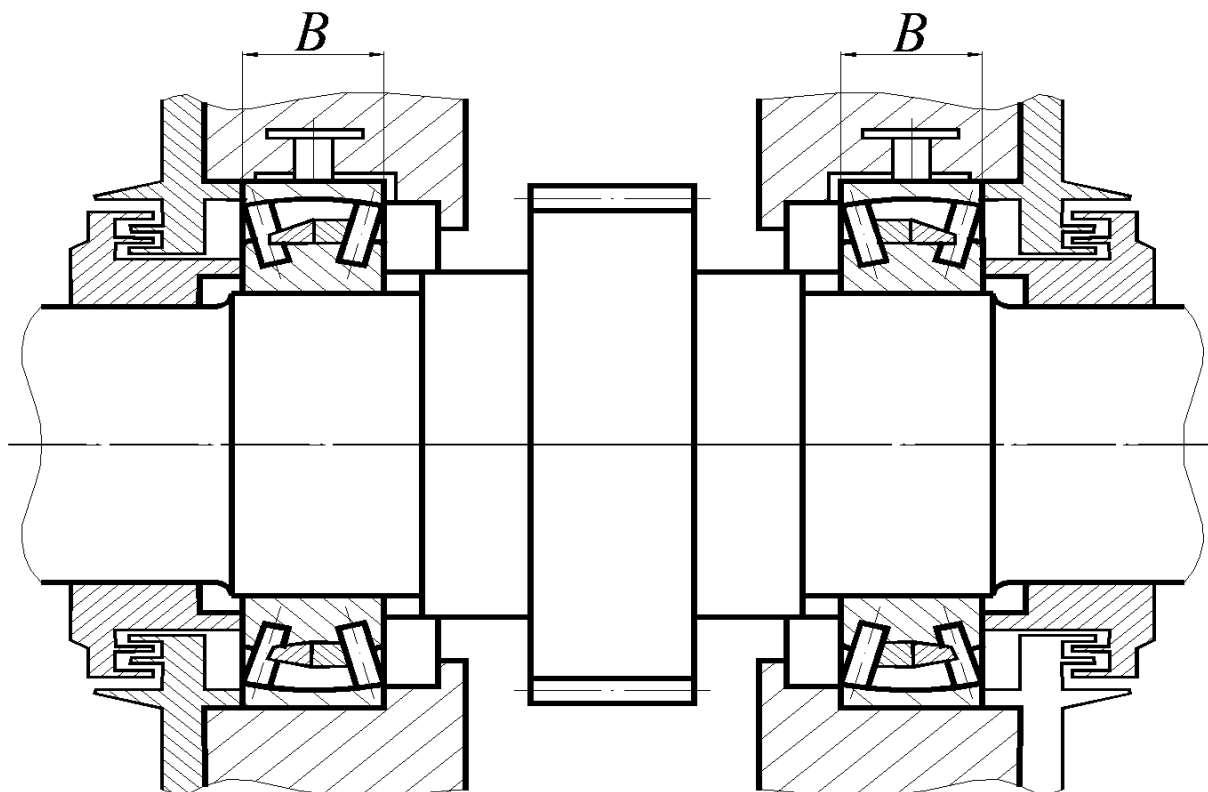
Конструкция части редуктора с роликоподшипниками
